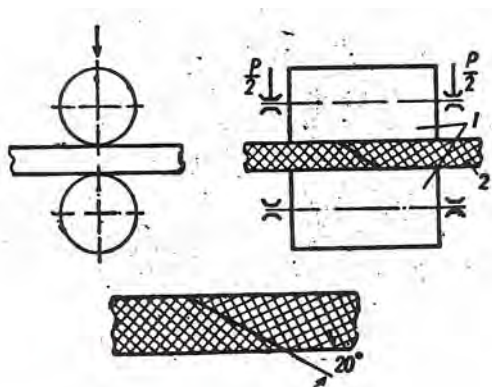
Схема сварки без присадочного материала: 1 - ролики; 2 - изделие
